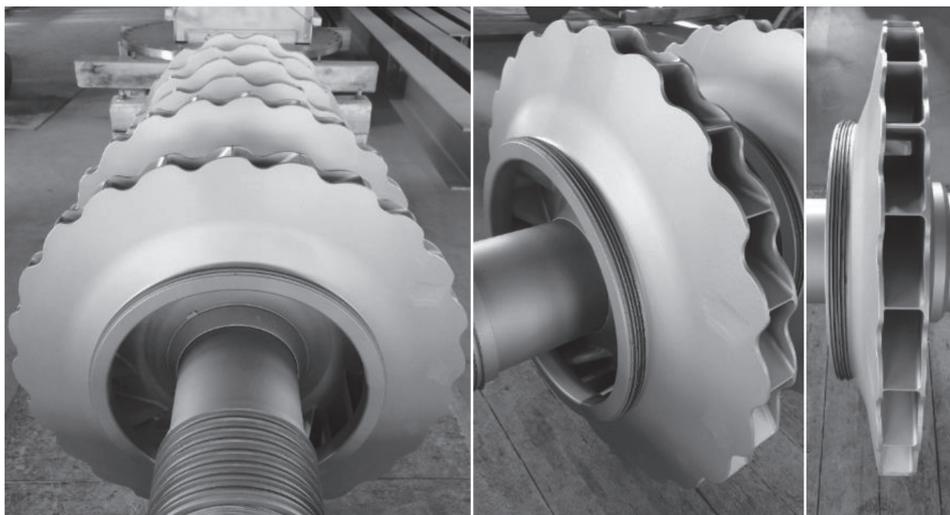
Модернизированный ротор ЦВД (компрессор типа К1290-121-1)
